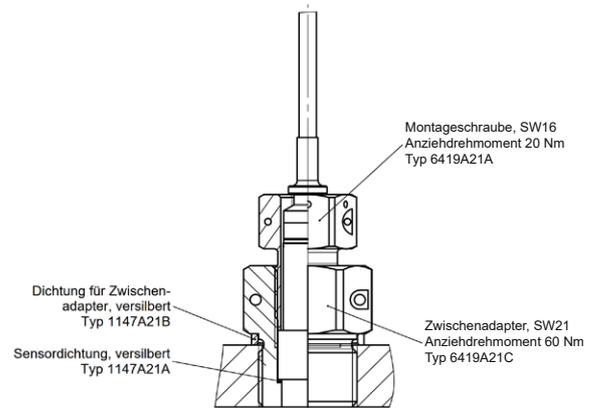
Montage mit Zwischenadapter Typ 6419A21C, Montageschraube Typ 6419A21A sowie Dichtung Typ 1147A21A und 1147A21B
